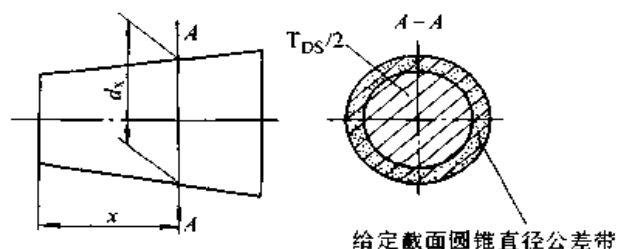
给定截面圆锥直径公差及公差带
